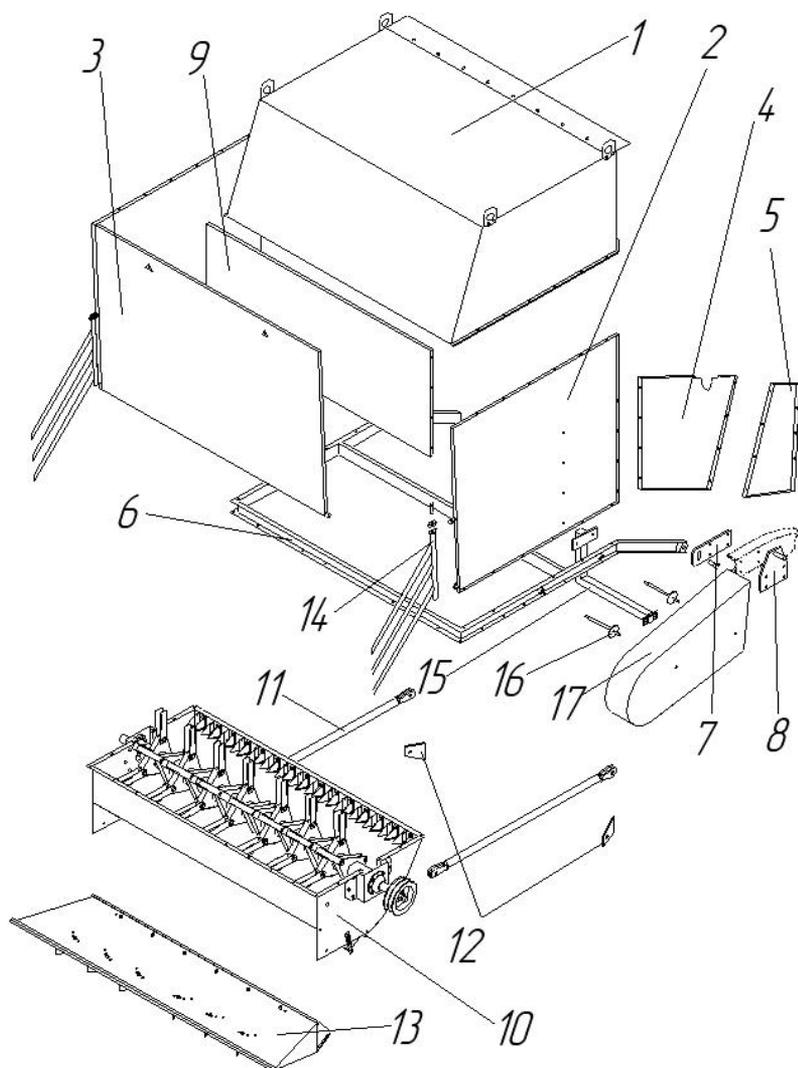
Устройство, схема монтажа и сборки измельчителя.
